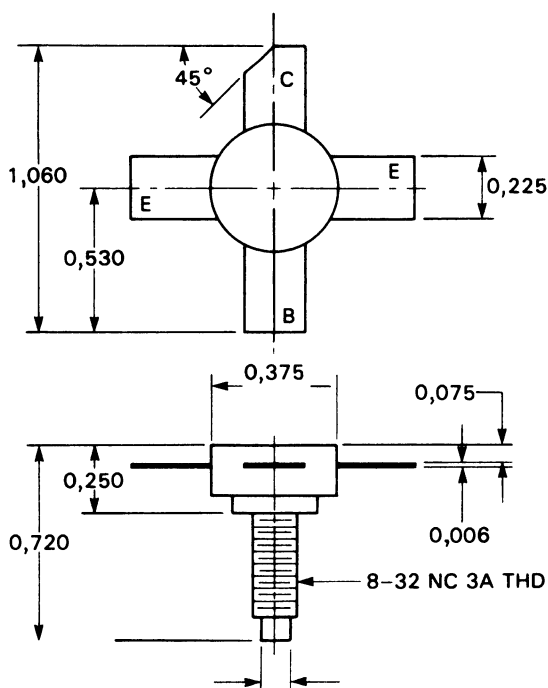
Корпус для мощного ВЧ-транзистора.
